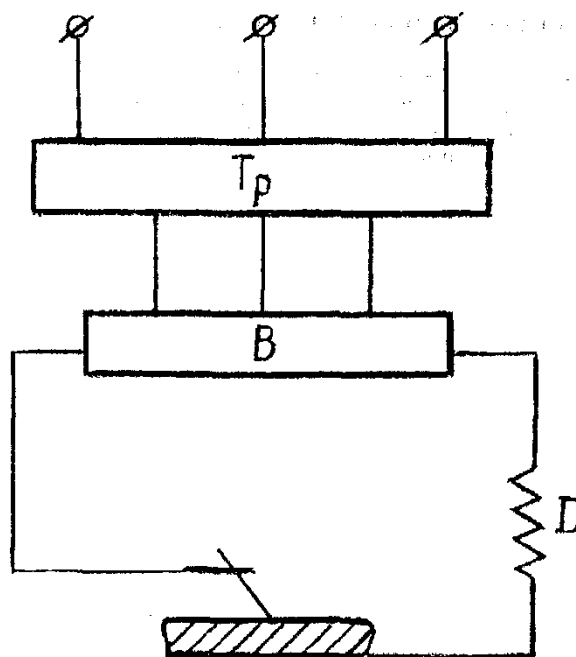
Принципиальная схема сварочного выпрямителя: Тр - понижающий трансформатор; В - выпрямительный блок; Д - дроссель
